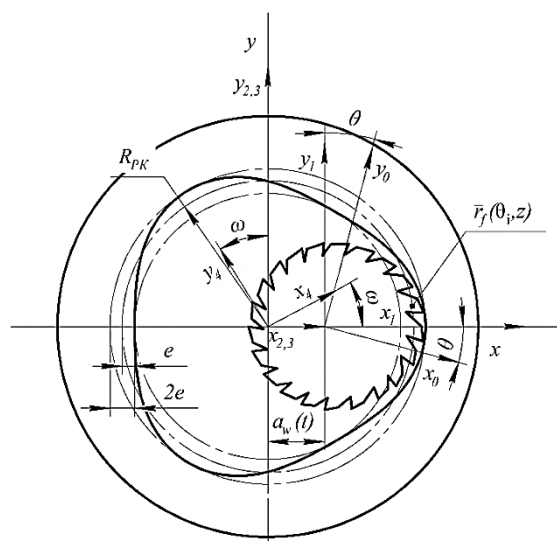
Схема обработки РК-3 отверстия фрезой с переменным радиусом
